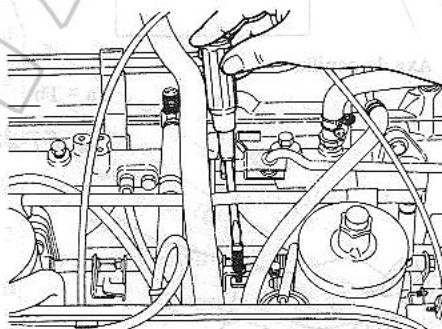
Desserrage de la vis de réglage d'équilibrage
